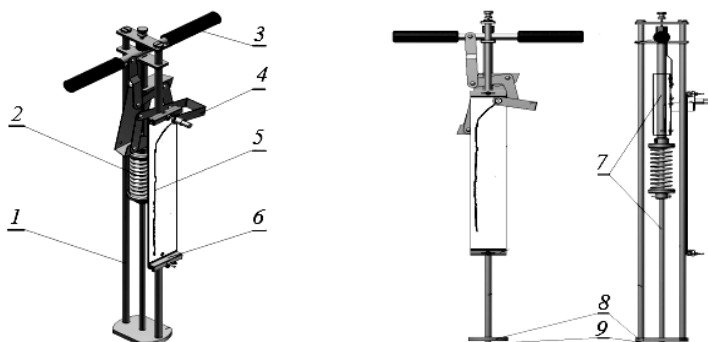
Общий вид твердомера Ю. Ю. Ревякина:
